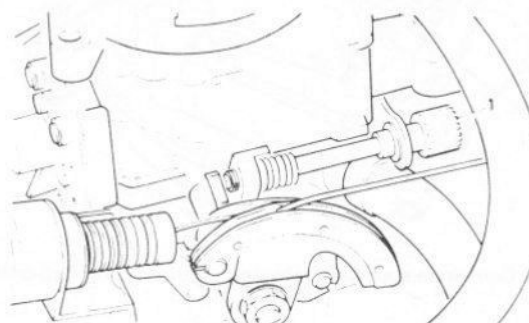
Vis de réglage de ralenti (1) - carburateur Weber 36 TLC (Sec 8)
